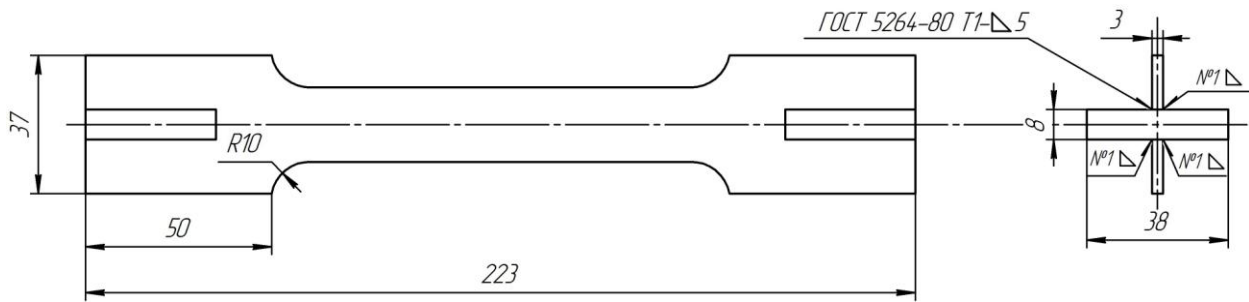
Чертеж образца из стали Ст3 для испытаний на одноосное растяжение.
